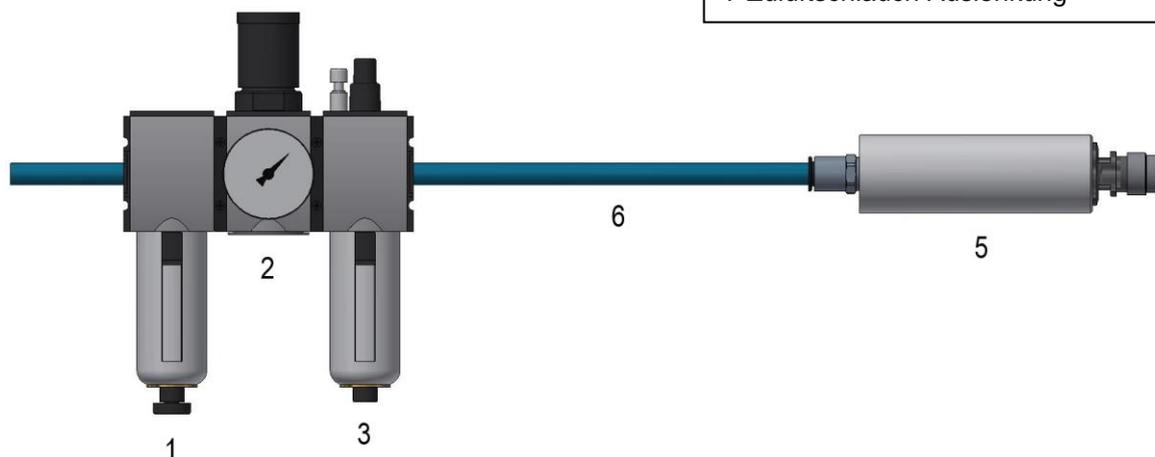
Anschluss Schleifspindel starre Ausführung
